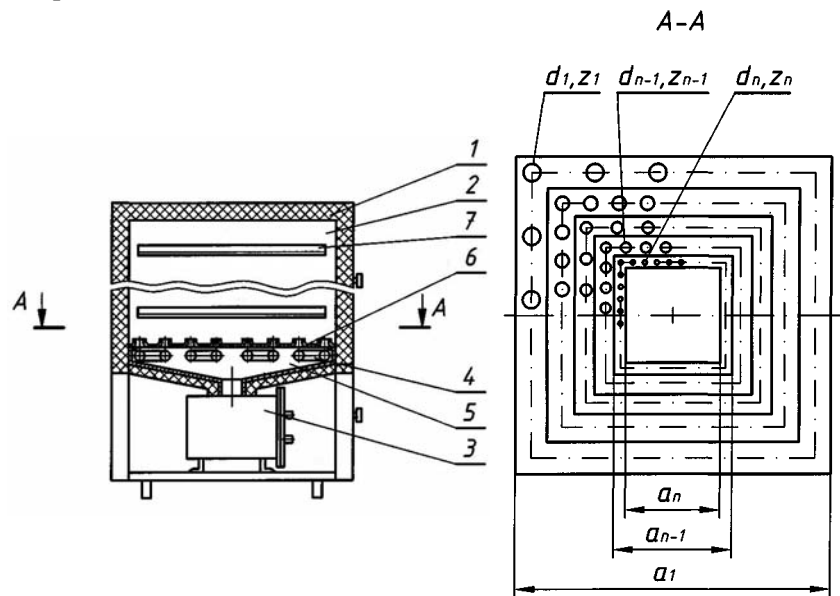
Схема пароварочной камеры: 1 – корпус; 2 – рабочая камера; 3 – парогенератор; 4 – электронагреватели; 5 – коллектор; 6 – панель перфорированная; 7 – направляющая; d_n – диаметр отверстий в n -м условном кольце; Z_n – количество отверстий в n -м условном кольце; a_n – длина стороны в n -м условном кольце
